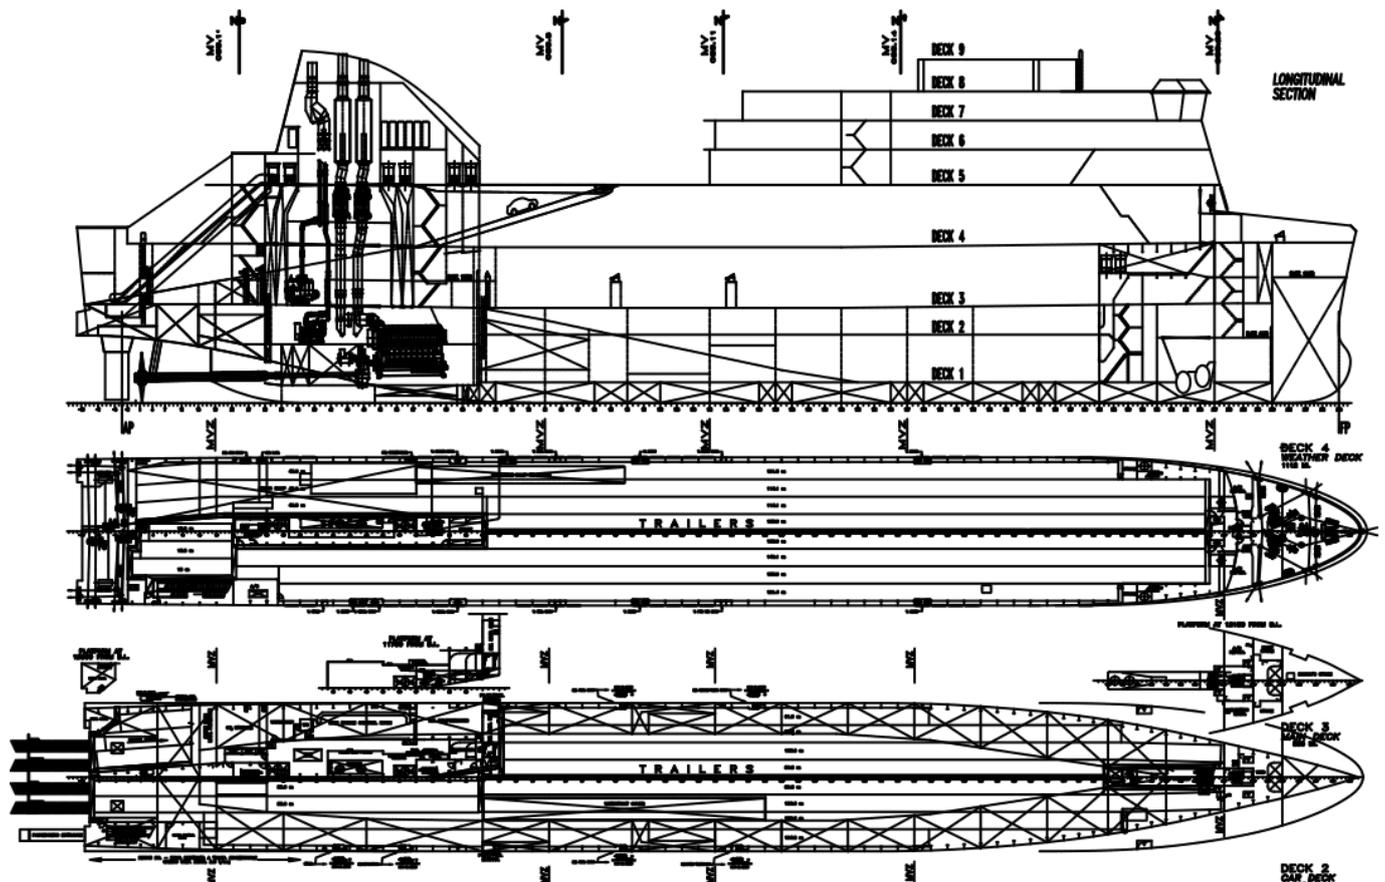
Plano de disposición general, parcial, del CIUDAD DE PALMA. Solamente se muestran vistas de perfil y planta de las cubiertas 3 y 4.
